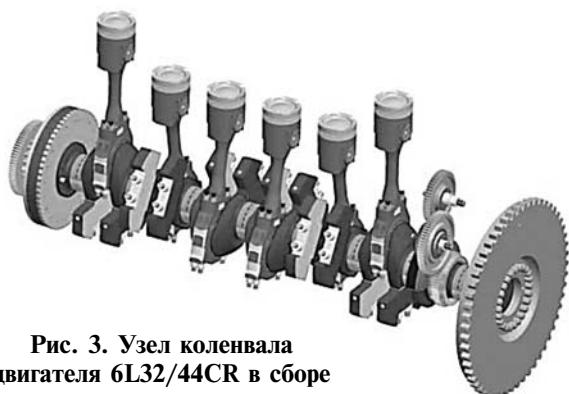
Узел коленвала двигателя 6L32/44CR в сборе
